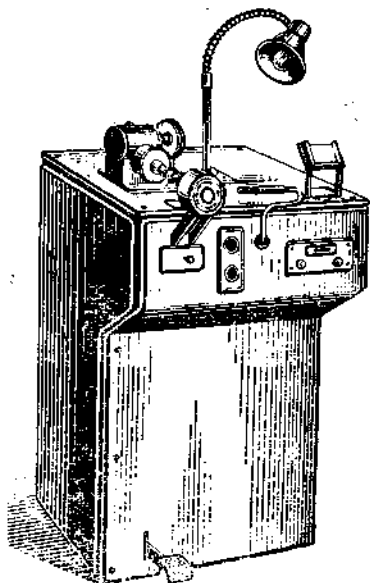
Станок типа СЗ для скрутки, подрезки и сварки жил проводов и проверки заготовок проводов
